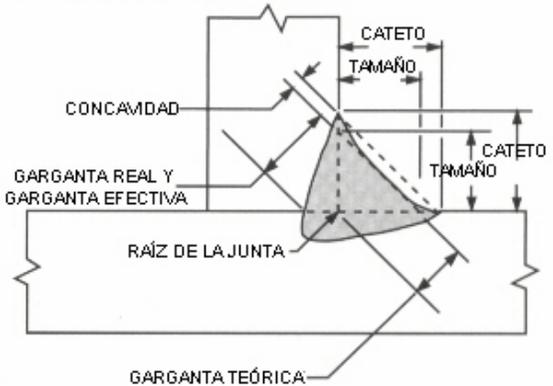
Penetración y tamaño de la soldadura
